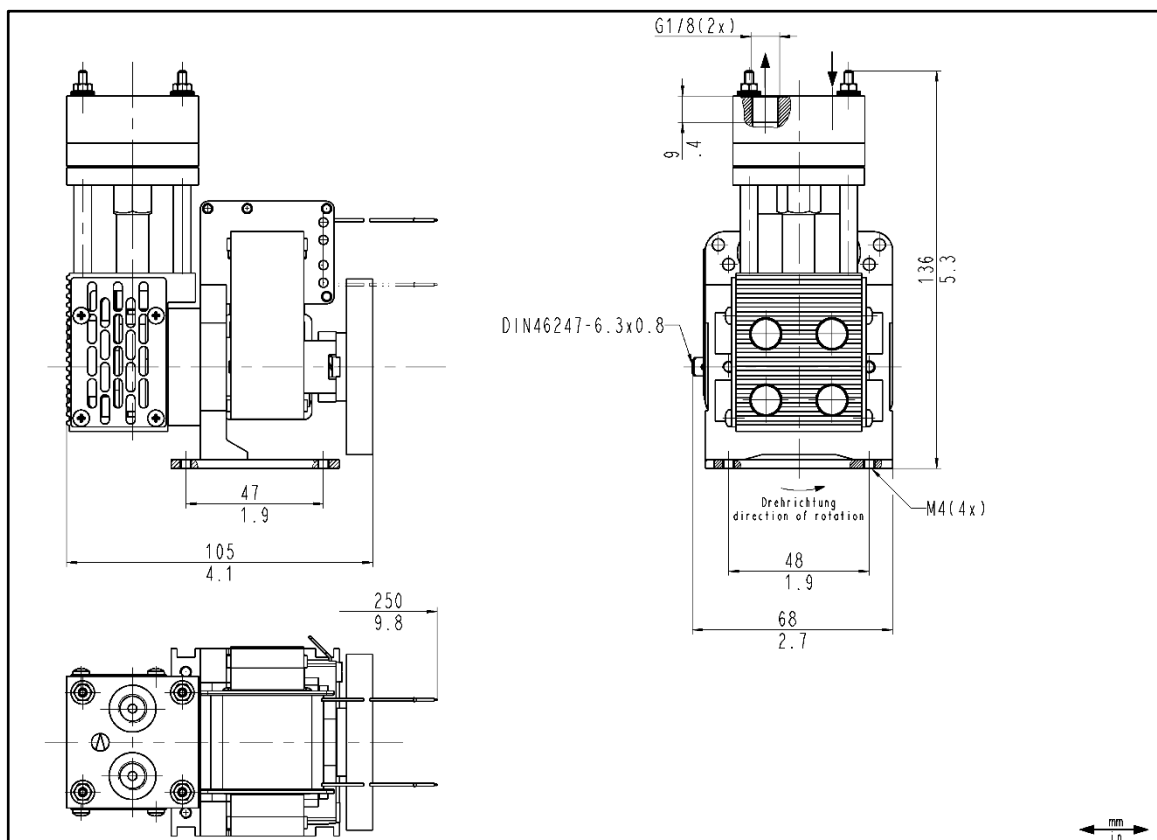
Befestigungsmaße Pumpenreihe N86.16
